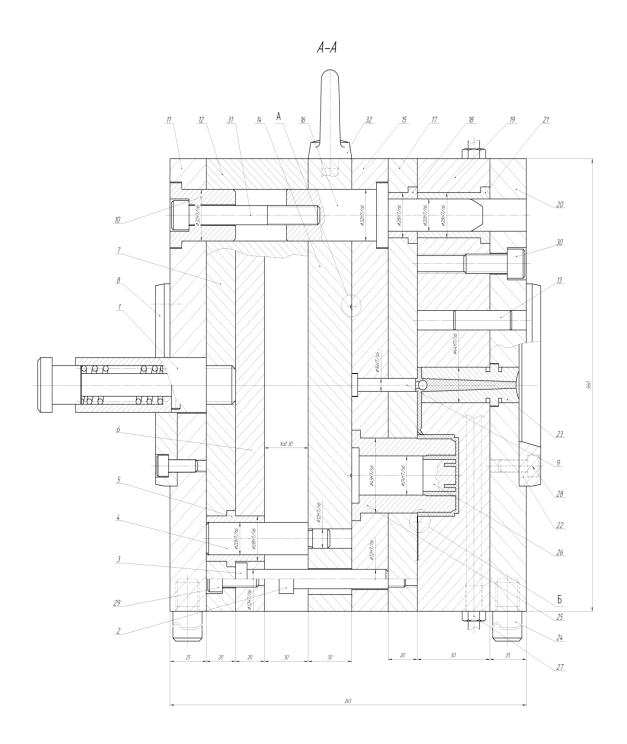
Литьевая форма новой технологии изготовления детали «Крышка бака топлива» (в разрезе A-A)
